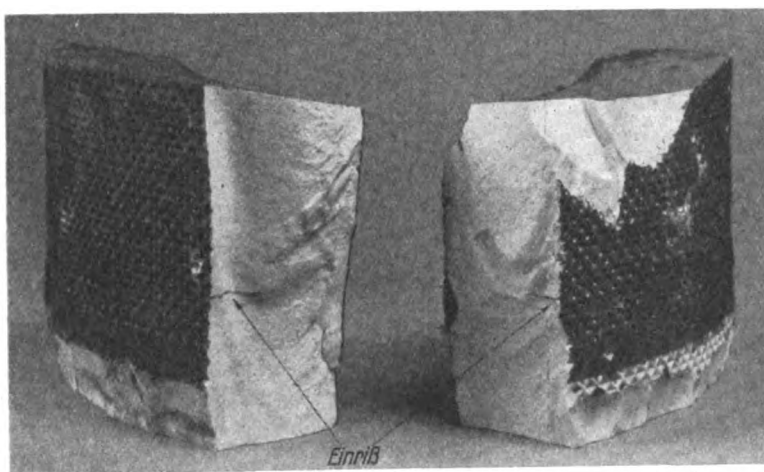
Eingefärbte Bruchstücke mit Einrißstelle.
